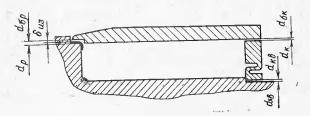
Обозначения посадочных диаметров бандажного и центрирующего колец, бочки и вала ротора для заполнения формуляра.
